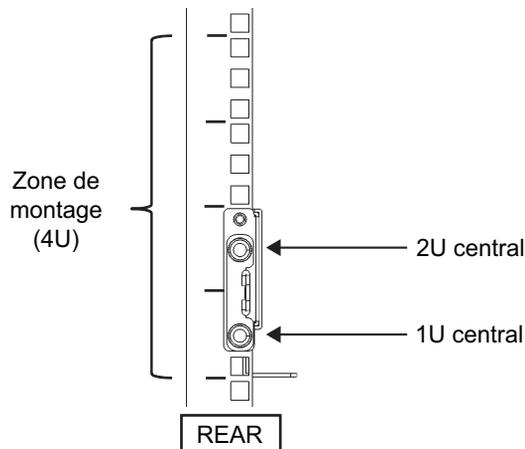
Fixation solide d'un dispositif de fixation de support de câbles et d'un rail
